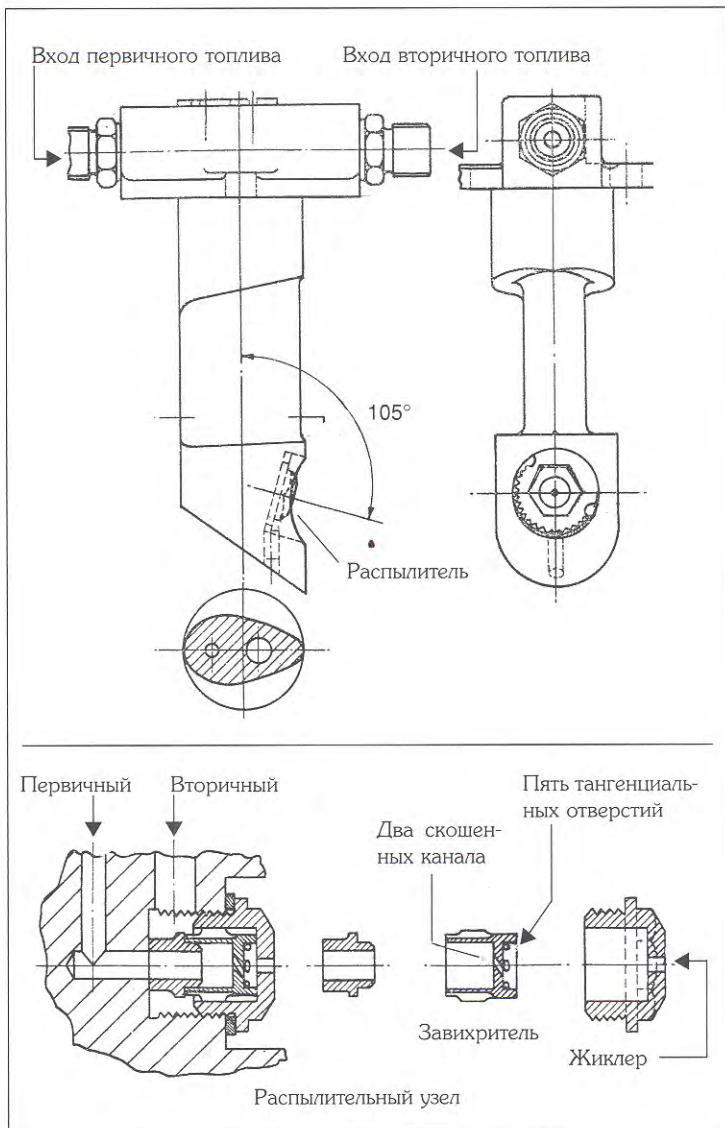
Дуплексная топливная форсунка для двигателя 109-011 A-0
